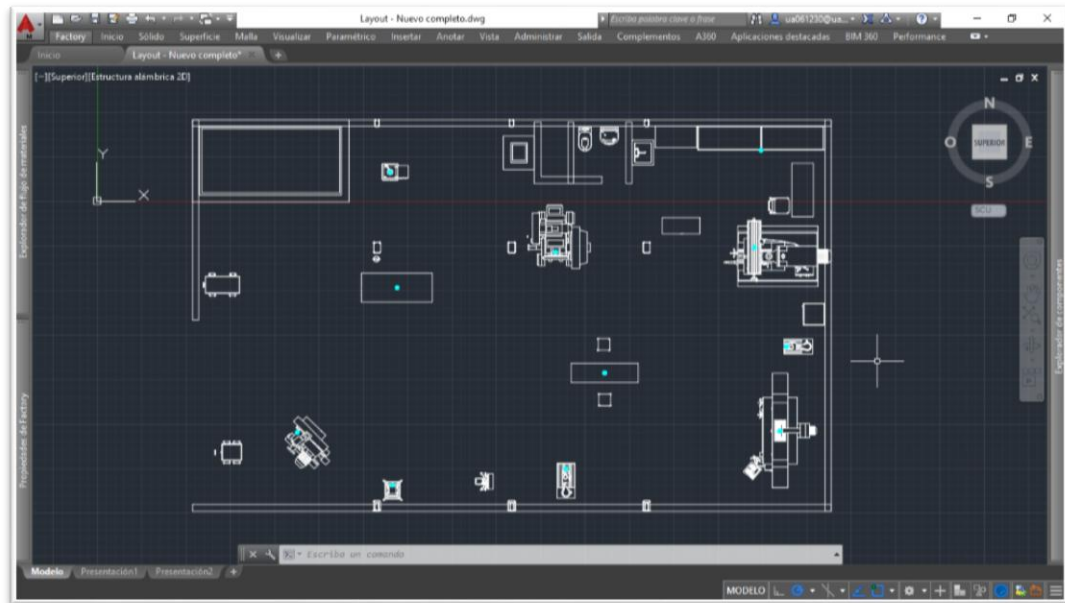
AutoCAD Mechanical 2016 versión Factory Design.
